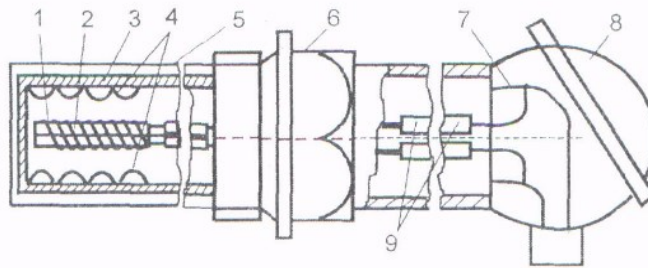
Конструкція металевого термометра опору: 1 - терморезистивний чутливий елемент; 2 - каркас; 3 - алюмінієва гільза; 4 - пружні металеві пластини; 5 - чохол; 6 - штуцер; 7 - провідник; 8 - з'єднуюча головка; 9 - ізоляційні буси
